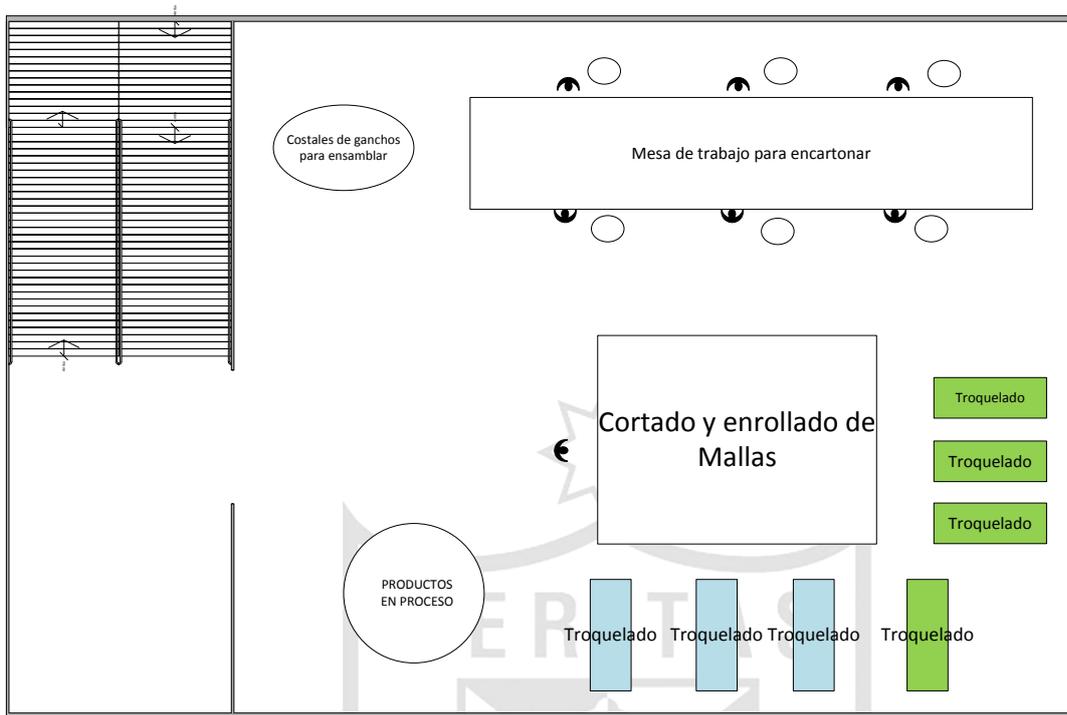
Plano: Vista de Planta del 2do piso LEÓN PLAST
